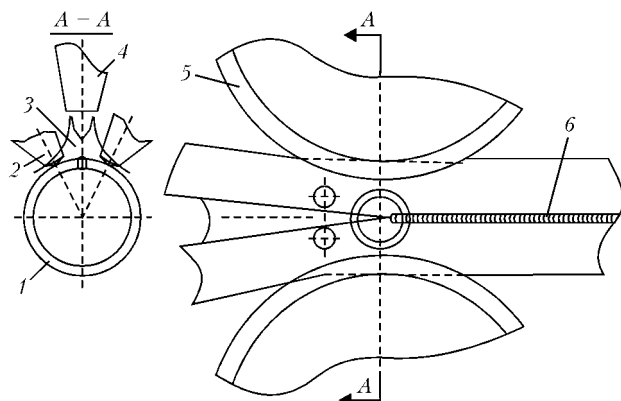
Схема шовной сварки труб с местной защитой зоны нагрева водородным пламенем: 1 — свариваемая заготовка; 2 — токоподводы; 3 — восстановительная зона пламени; 4 — сопло подачи водорода; 5 — формирующие валки; 6 — сварной шов
